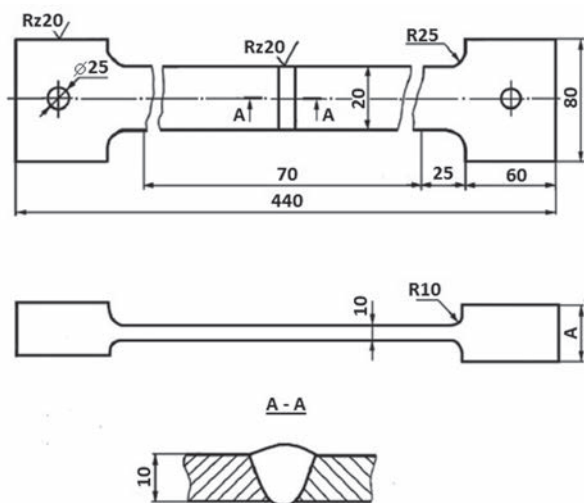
Плоские образцы со стыковыми сварными швами
